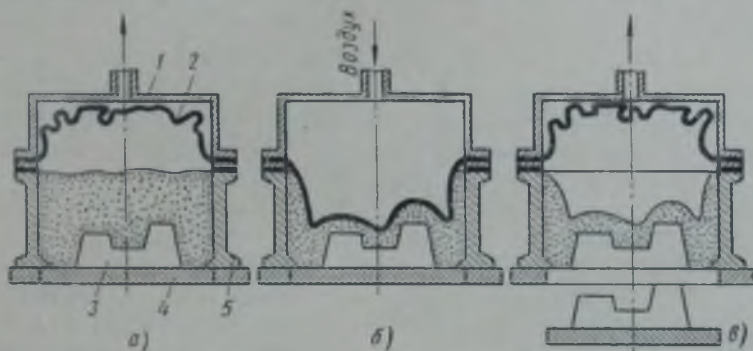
Схема уплотнения формовочной смеси резиновой диафрагмой:
